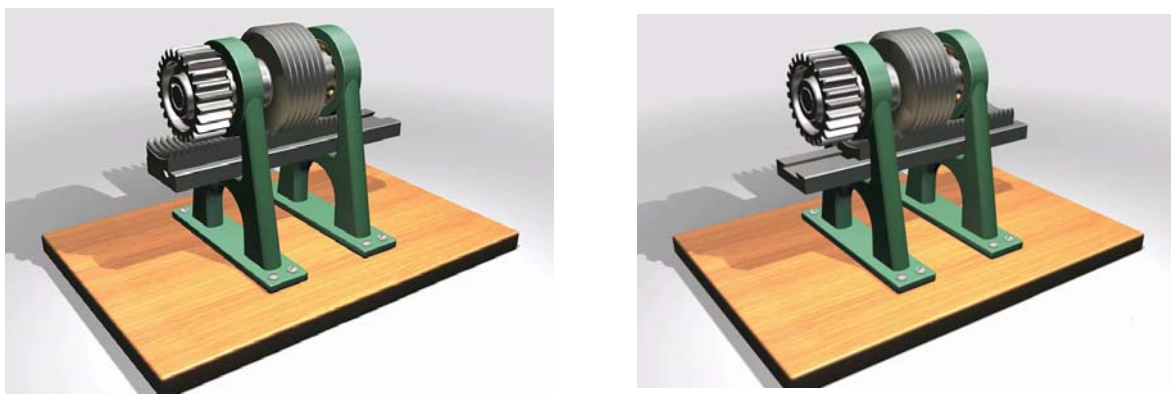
3D модель черв'ячно-рейкової передачі (рейка рухома)
